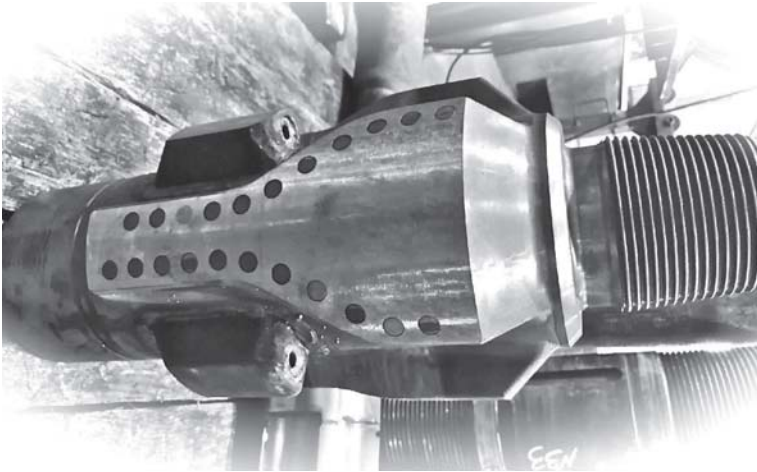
Опытный образец калибратора-эжектора КЭ215,9-3Л
